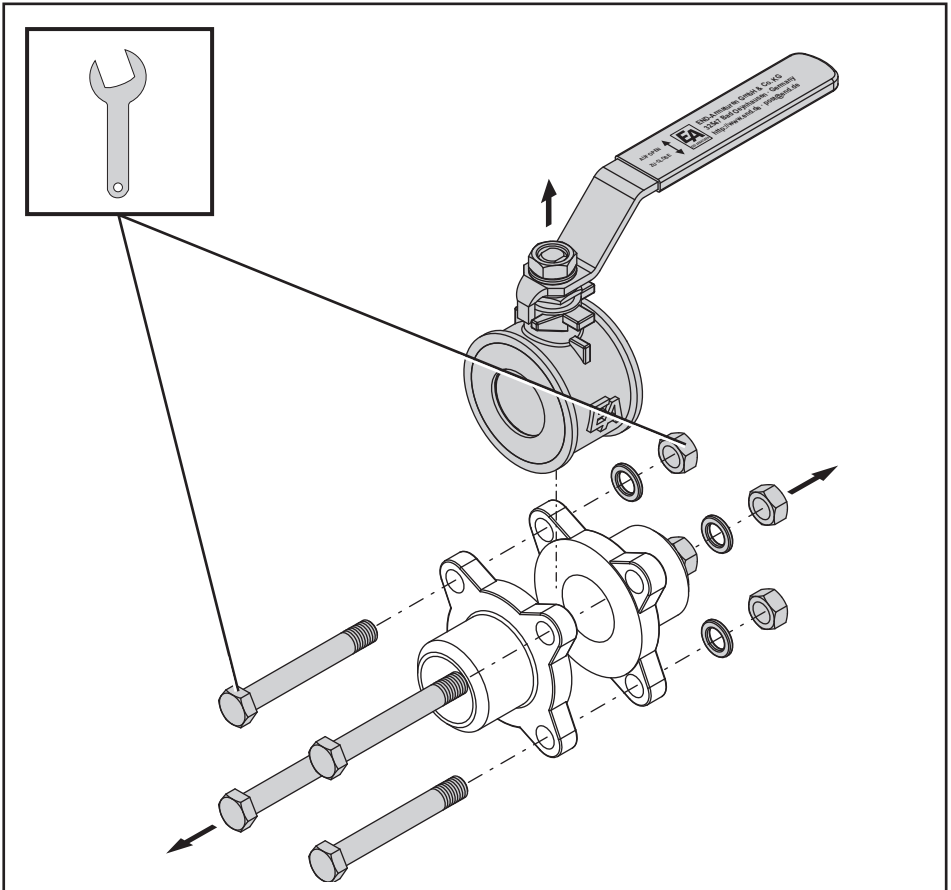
Kugelhähne, Montage Anschweißenden, Demontage des Kugelhahnmittelteils (Abbildung zeigt Art. ZE311064)
